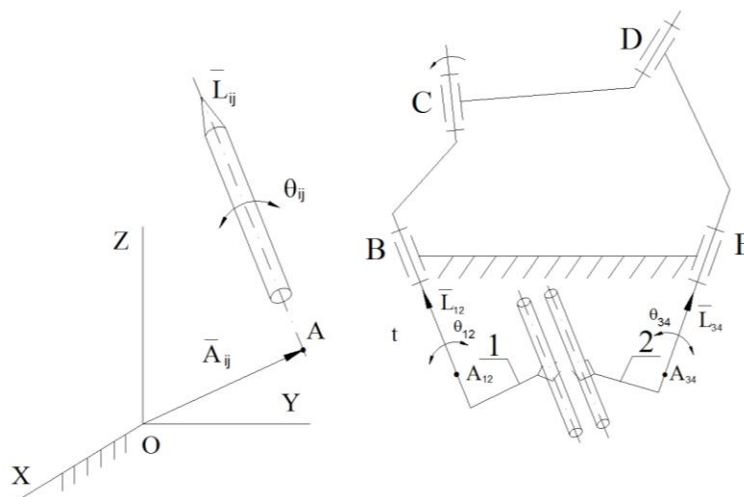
Пространственный четырехзвенный сборочный манипуляционный механизм, предназначенный для сборки длинных деталей типа тел вращения
